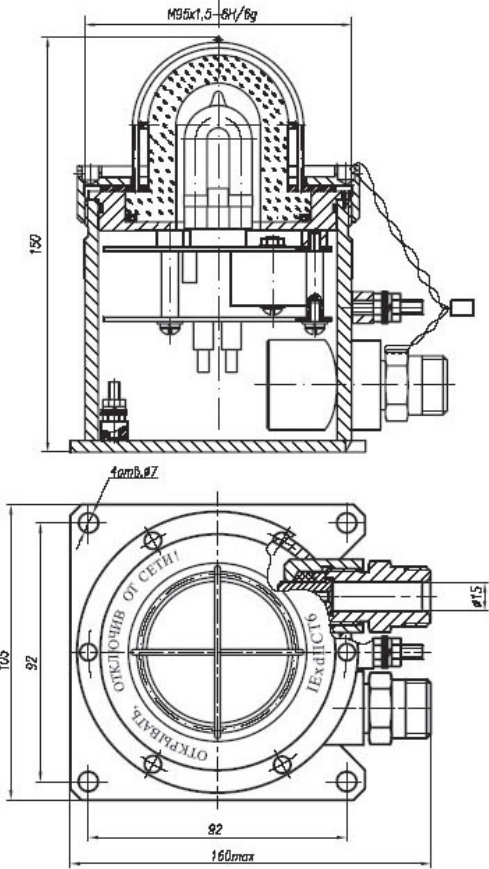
Габаритный чертёж светового Оповещателя ЕхОППС-1В-СМ в алюминиевом корпусе
